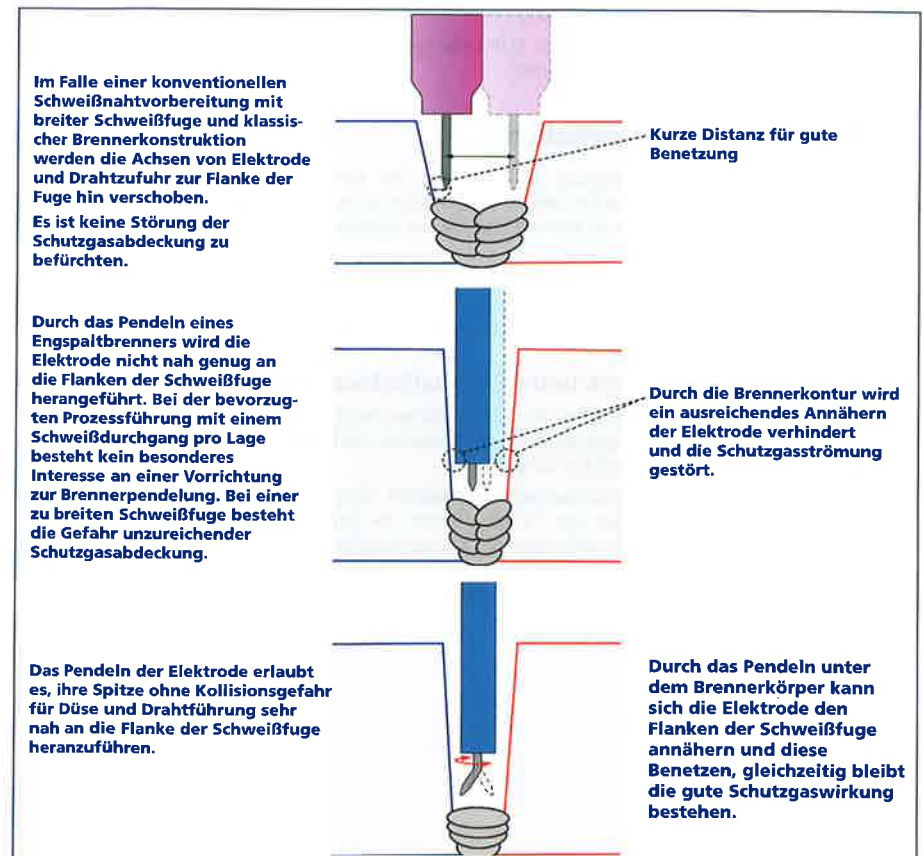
Prinzip und Vorteile des WIG-Schweißens mit gependelter Elektrode
